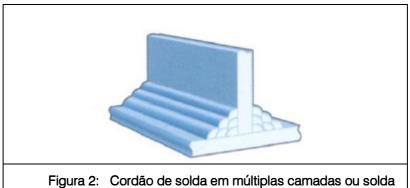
Cordão de solda em múltiplas camadas ou solda "espaguete".
